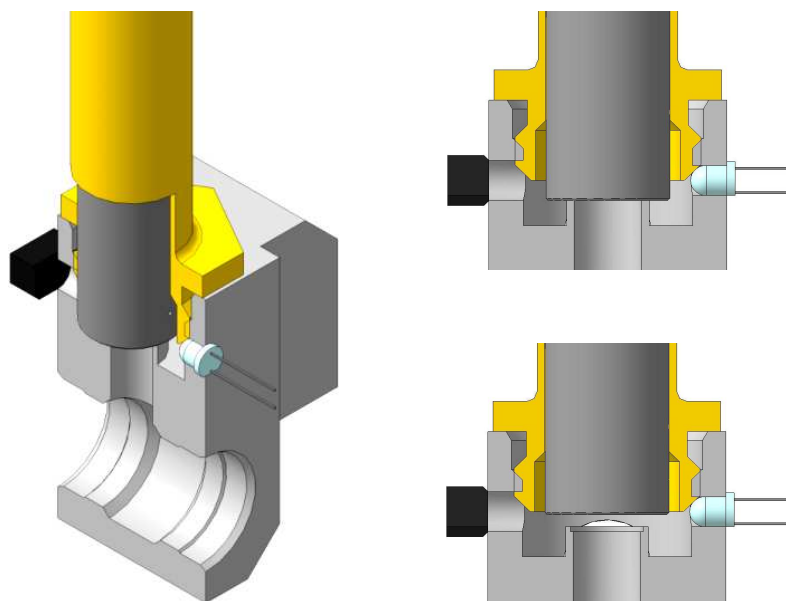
Розташування ДПГ в корпусі дозатора
